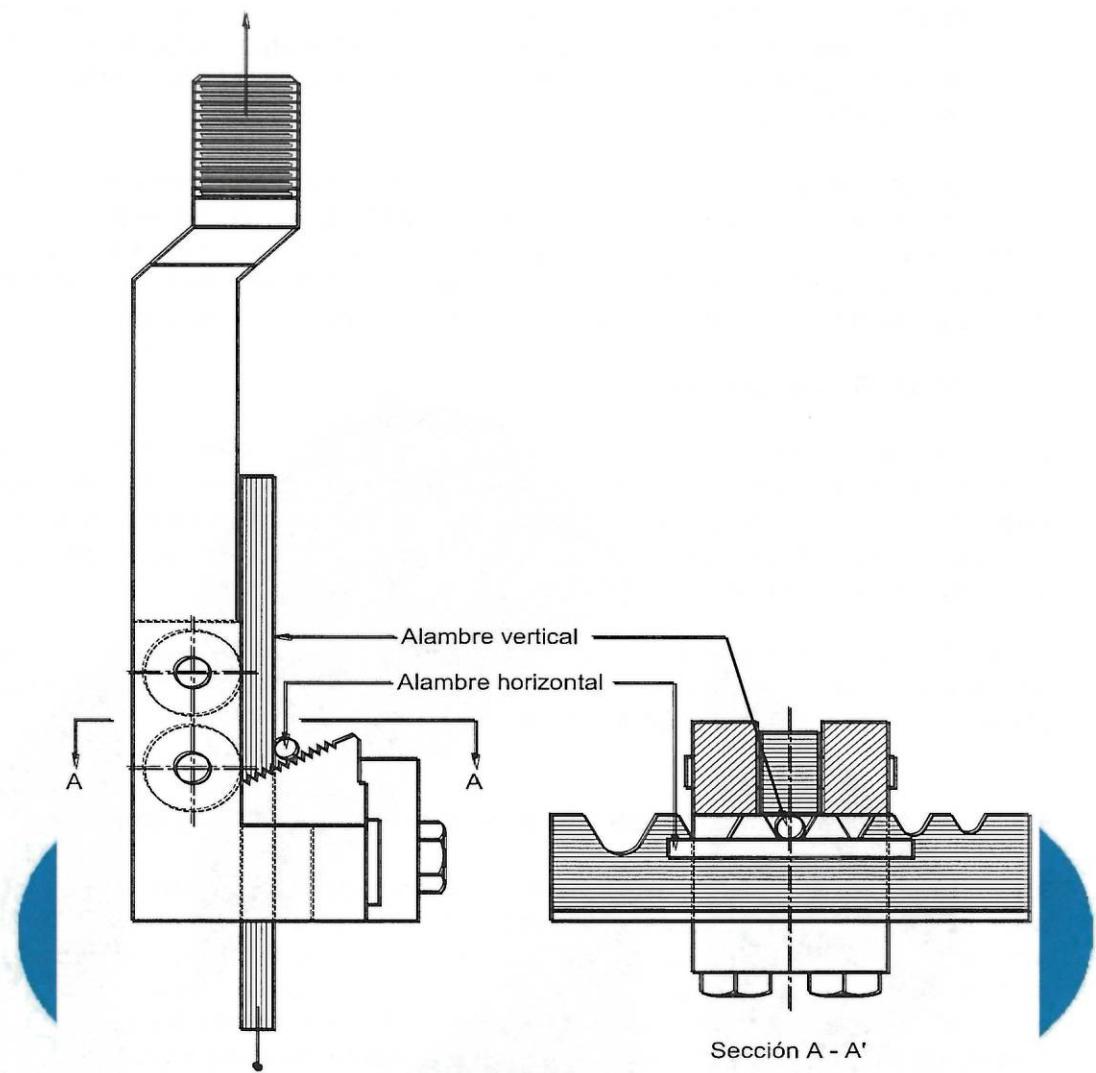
Dispositivo de ensayo para la soldadura de malla electrosoldada
